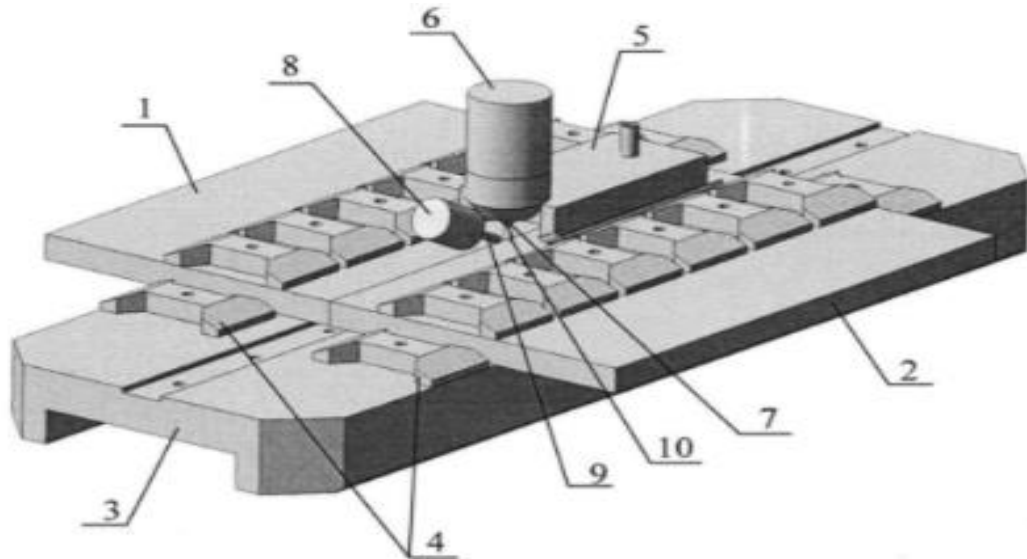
Схематичне зображення (3D схема) процесу аргонодугового зварювання за один прохід з присадочною дротом
